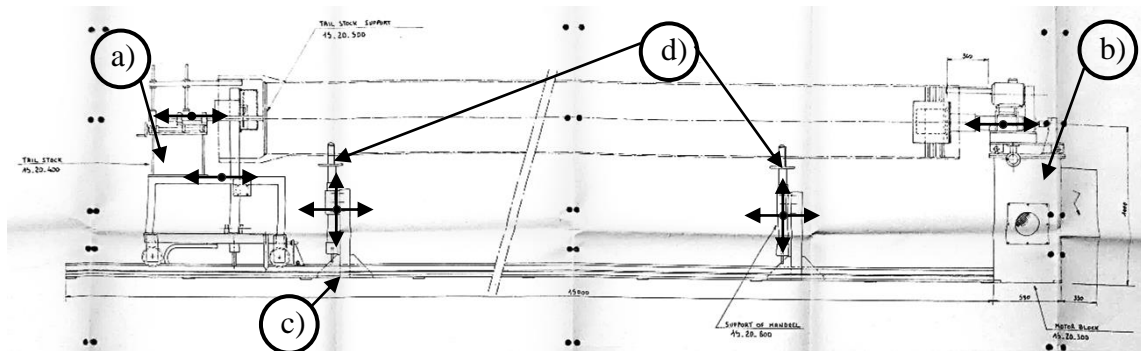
Vista total lateral da máquina existente na Vidropol, com destaque para os movimentos possíveis das diferentes partes da máquina e os principais componentes, a) Cabeçote fixo, b) Cabeçote móvel, c) Carril, d) Preguiças.
